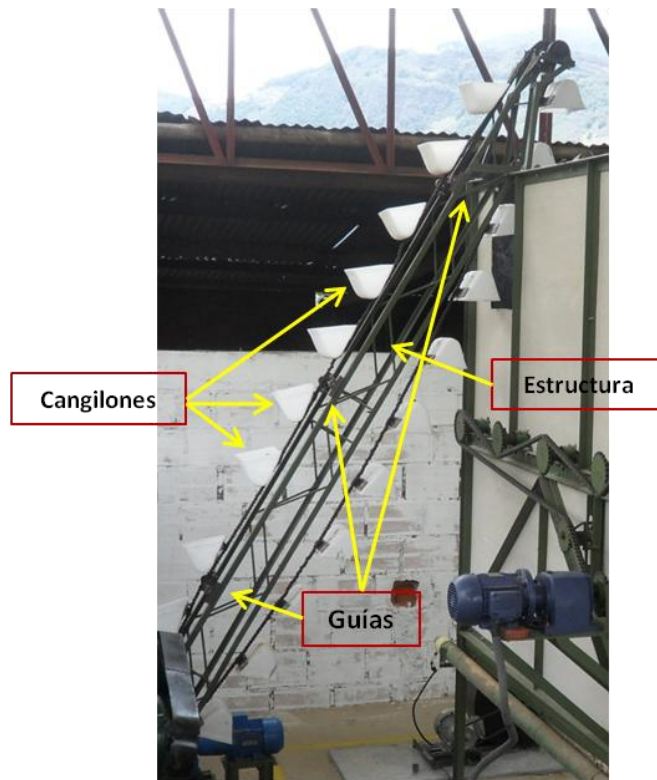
Sistema de transporte instalado. Fuente: el Autor
